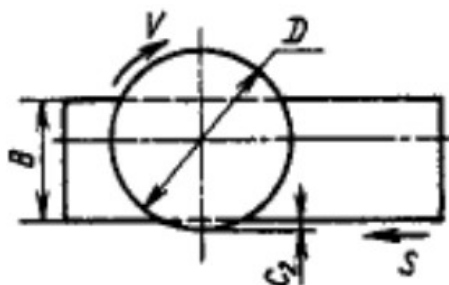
Расположение заготовки при торцовом фрезеровании
